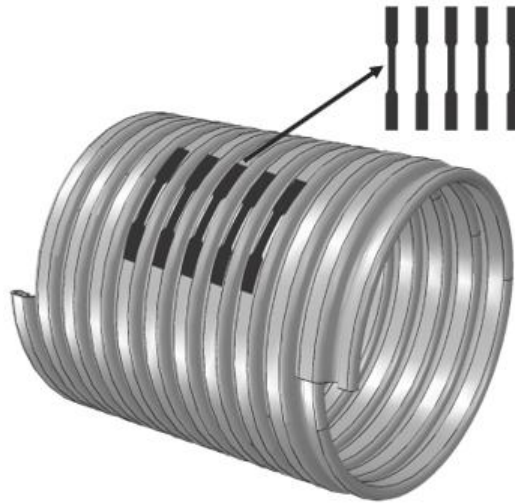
Corte e usinagem dos corpos de prova a partir da amostra de carcaça.
